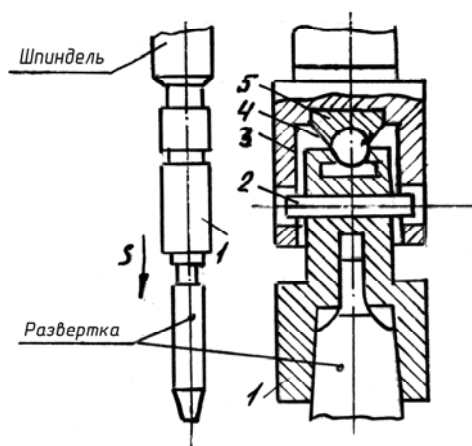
Качающаяся оправка для развертки: 1 - оправка; 2 - штифт; 3 - корпус; 4 - шарик; 5 - подпятник.
